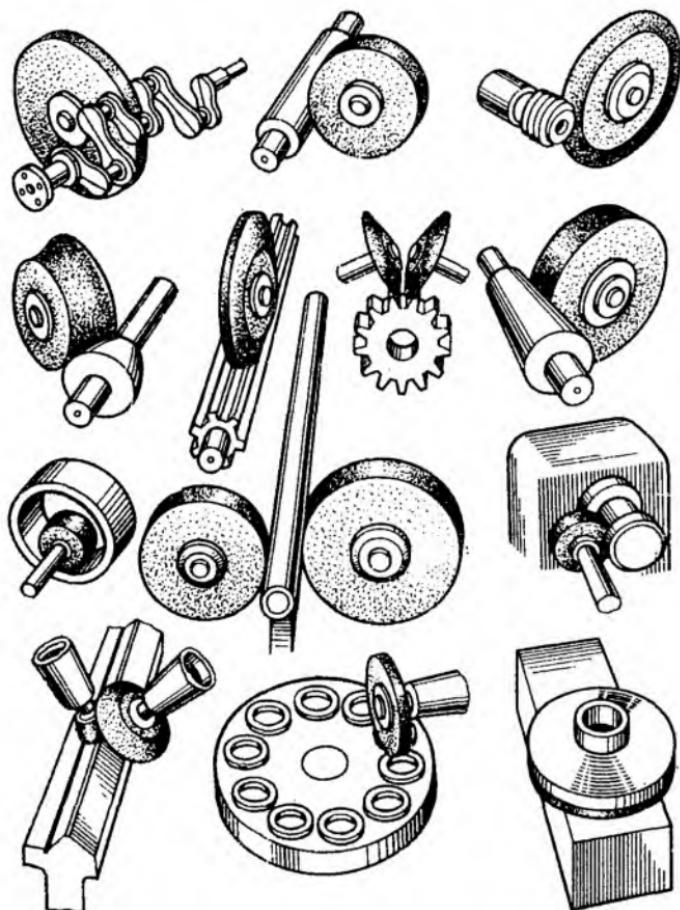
Типовые детали, изготавляемые на шлифовальных станках
